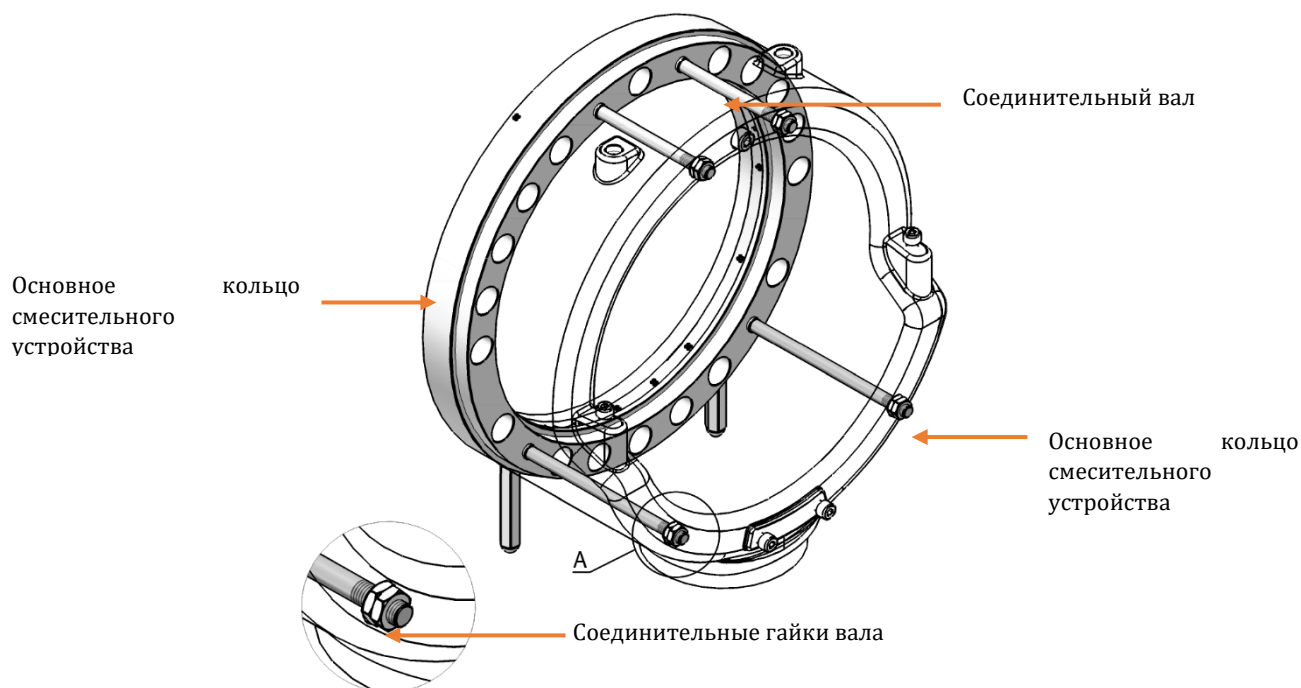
Монтаж удерживающего кольца газовых форсунок с основным кольцом смесительного устройства RGB-M-1350
